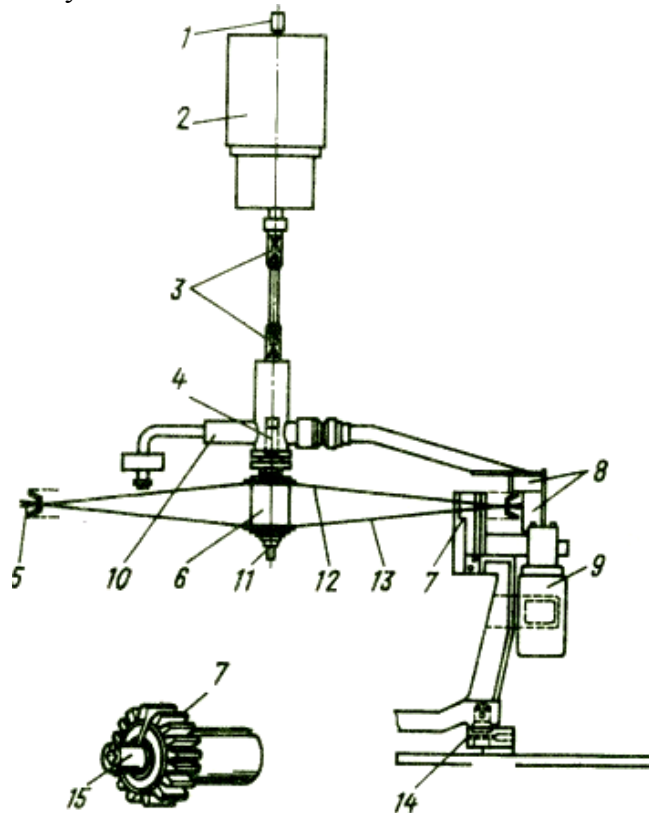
Сборочная машина с САУ для регулирования и контроля качества велосипедного колеса
